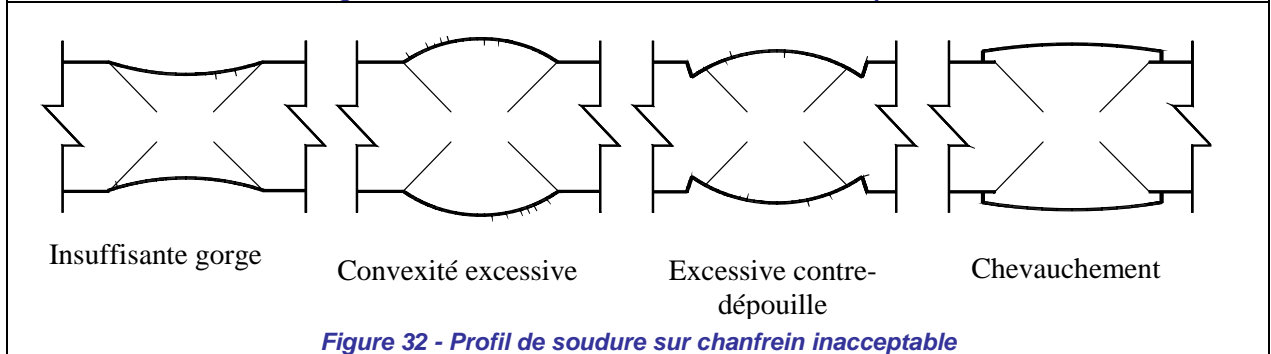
Profil de soudure sur chanfrein inacceptable
